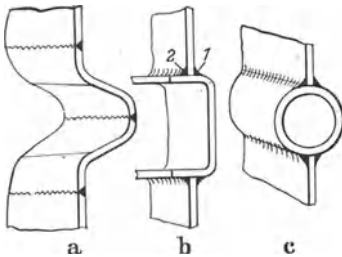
Ausgleichteile in zylindrischen Behältern.
